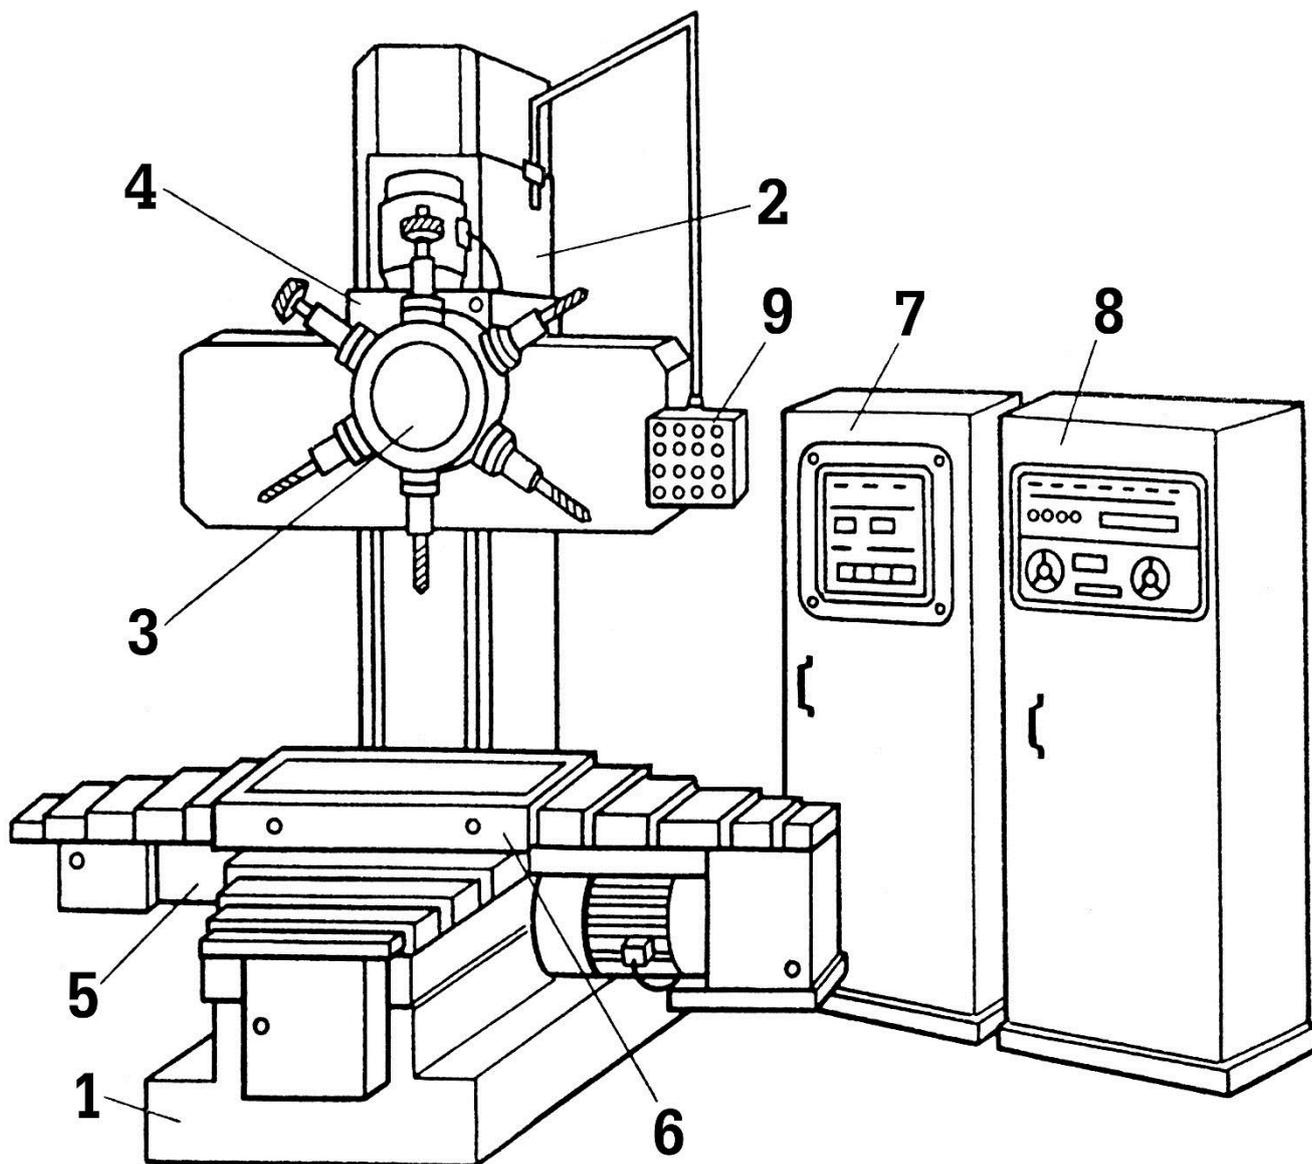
Основные части станка 2P135Ф2 - 1
